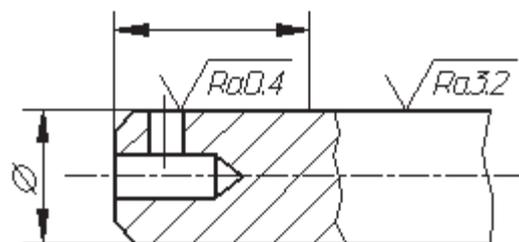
Пример обозначения различной шероховатости на одной поверхности
